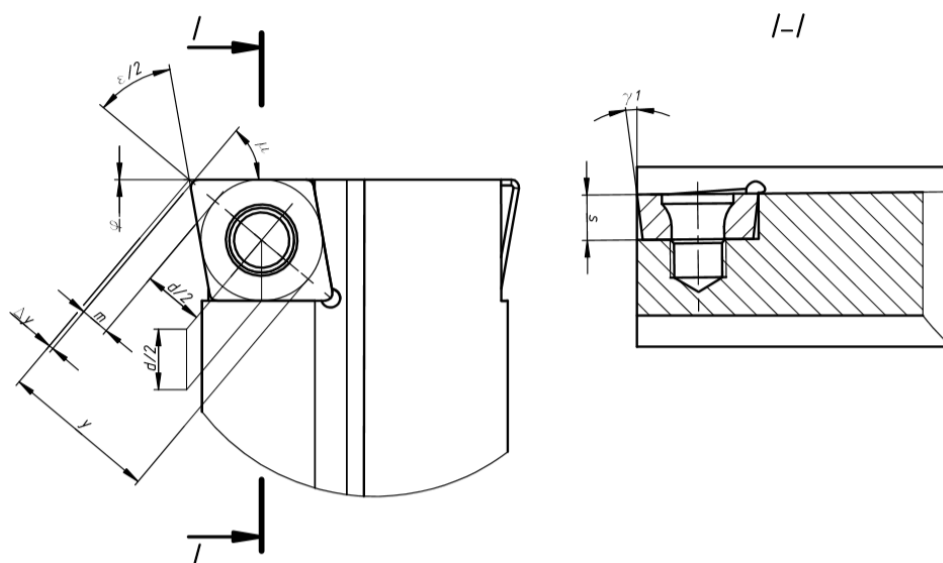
Розрахункова схема визначення похибки базування
